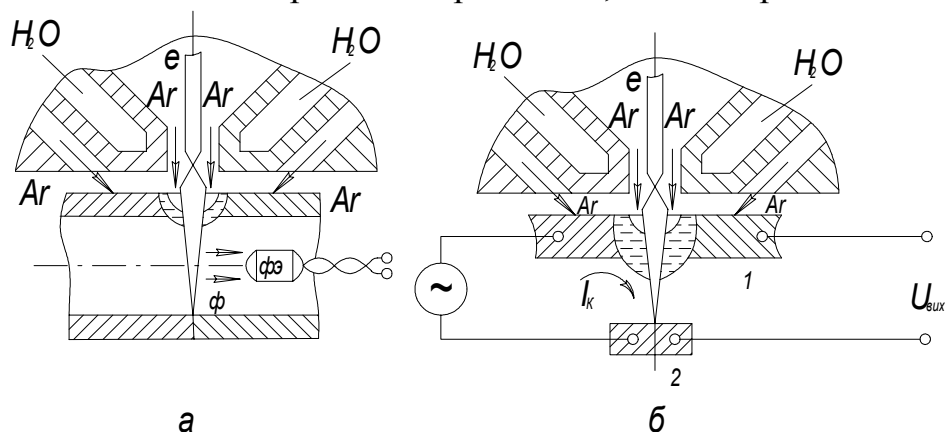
Способи контролю проплавлення при плазмовому зварюванні
